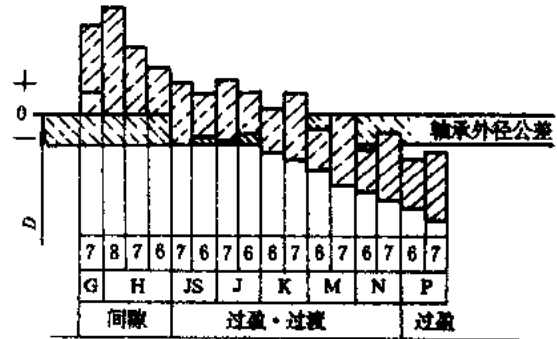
轴承与外壳孔配合常用公差带图
